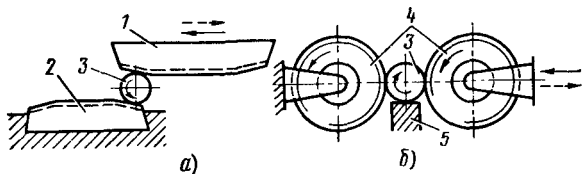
Схемы накатывания резьбы плоскими плашками (а) и роликами (б):
